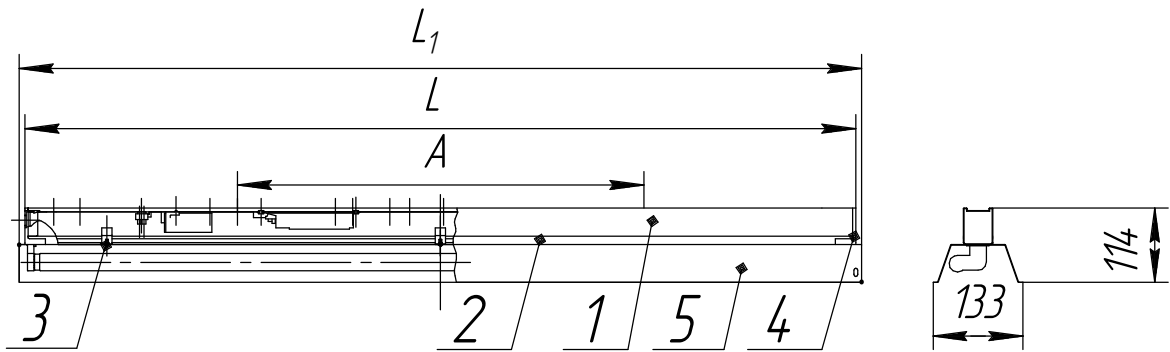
1. Корпус в сборе, 2. Крышка, 3. Винт, 4. Крышка, 5. Отражатель.
